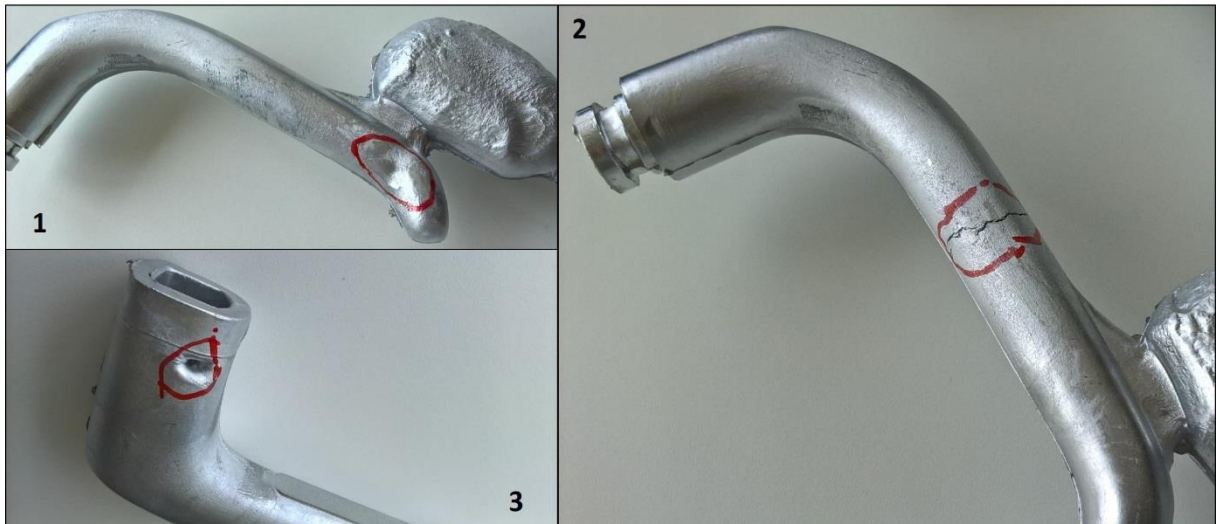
Defeitos do tipo Rechupe (1), Fissuras (2), e Mau Enchimento (3)
